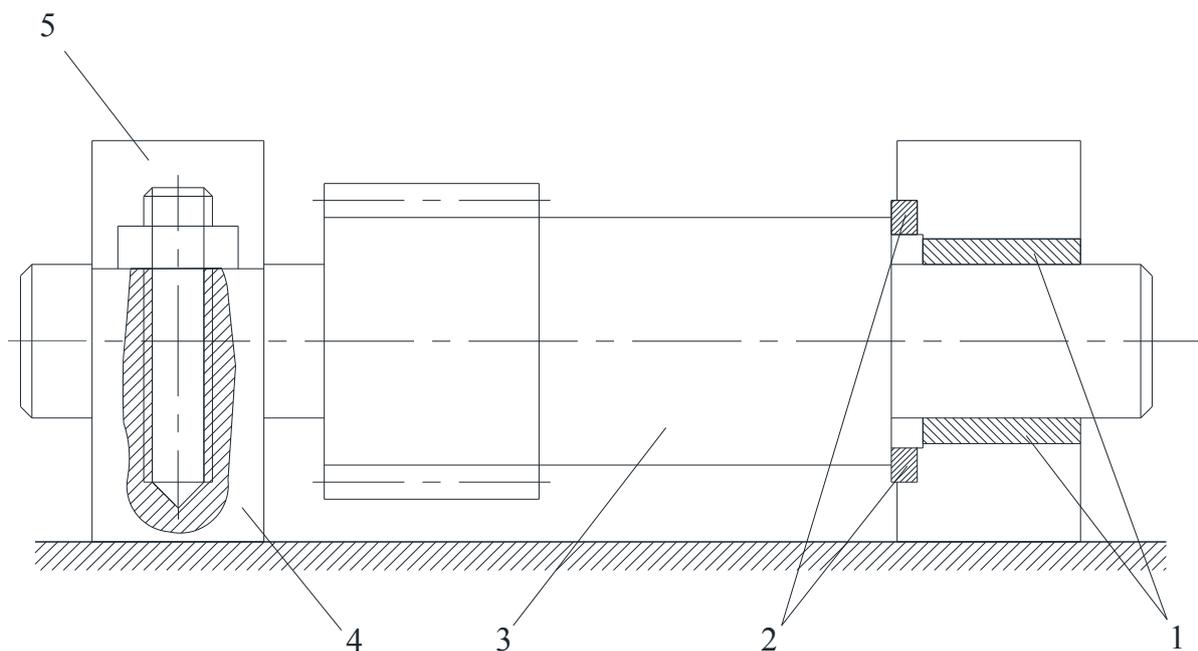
Схема установки для сборки валов и вкладышей: 1 – верхний и нижний вкладыши подшипника; 2 – верхний и нижний вкладыши упорных подпятников скольжения; 3 – вал-шестерня; 4 – корпус подшипника; 5 – крышка корпуса
